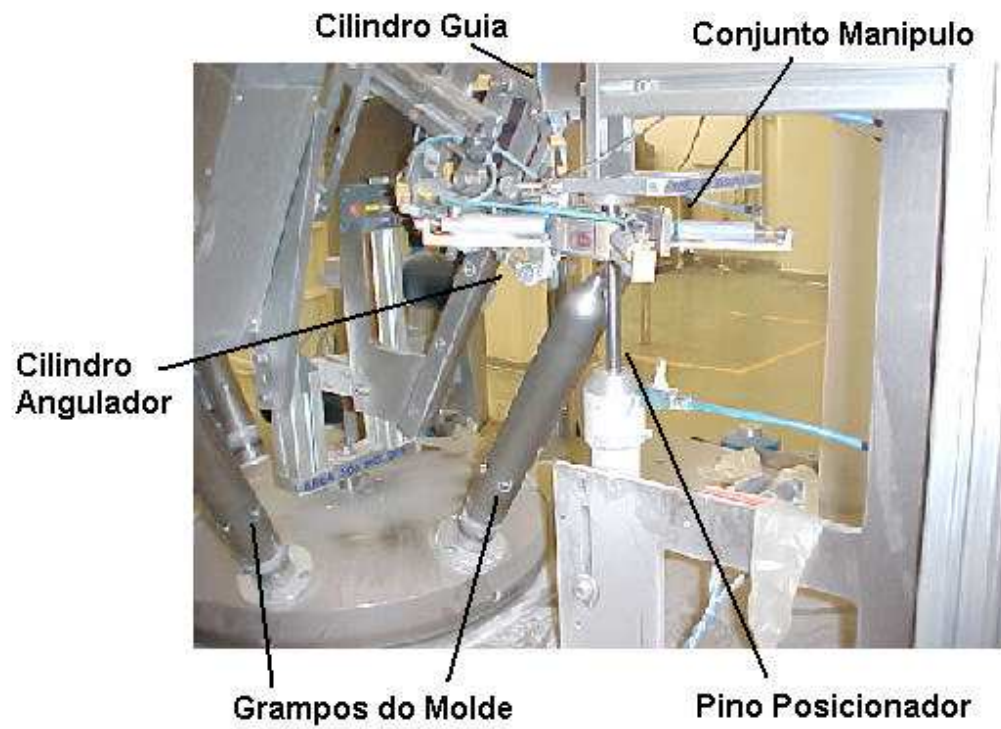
Conjunto de colocação Automático do Preservativo no Molde
